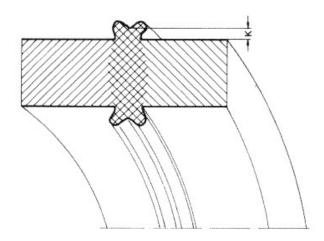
Вид грата при сварке нагретым инструментом.
